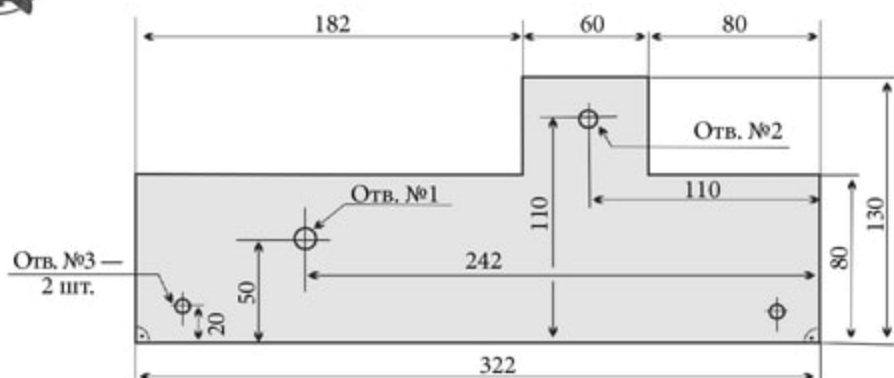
Чертеж средней опоры (деталь № 2) — 1 шт.
